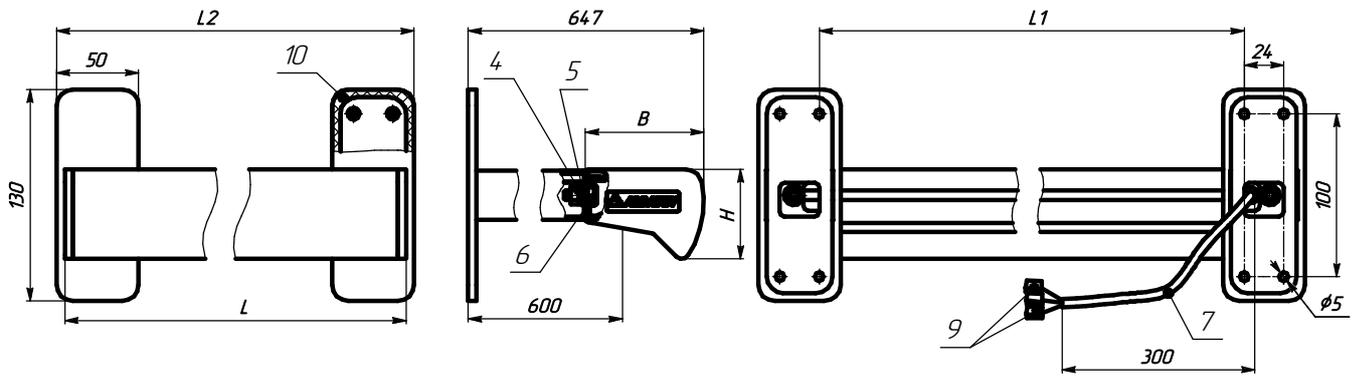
Габаритные и установочные размеры светильника ДБО43
